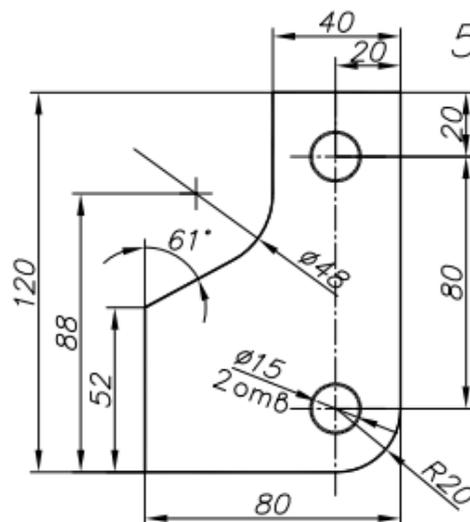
Эскиз детали для построения 3D модели (Эскиз.png)
